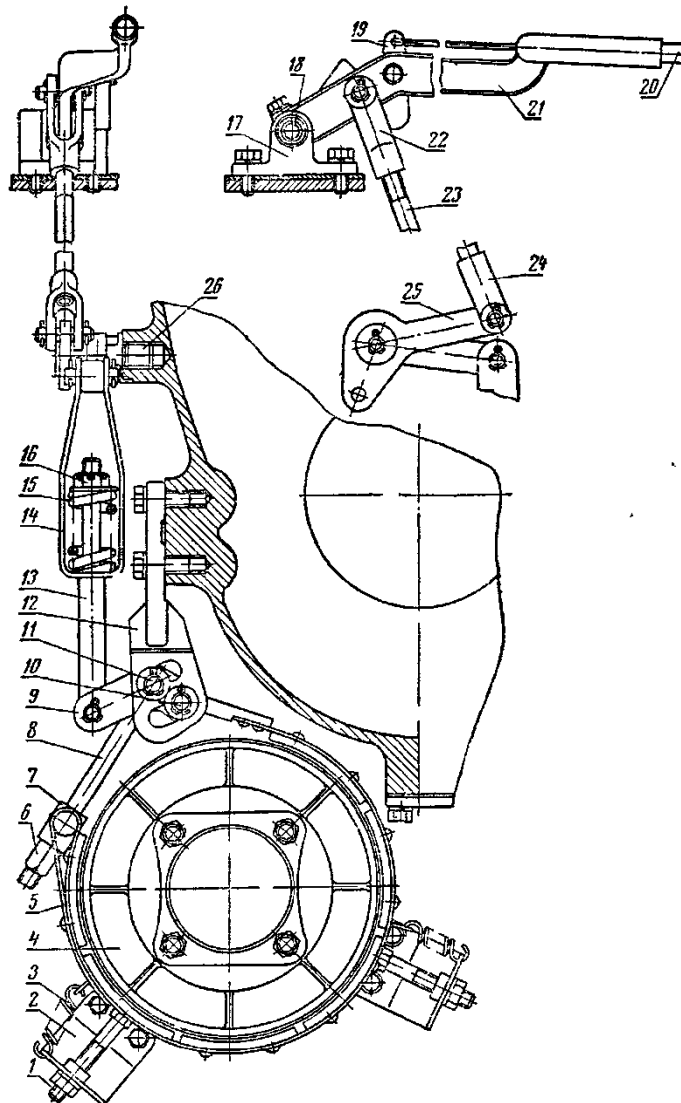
Центральный тормоз: 1 – регулировочный болт; 2, 12 и 17 – кронштейны; 3 – оттяжная пружина; 4 – барабан; 5 – лента и тормоза; 6 и 15 – гайки; 7 – втулка; 8 – регулировочная тяга; 9 и 25 – двуплечие рычаги; 10 и 11 – пальцы; 13 – тяга компенсатора; 14 – корпус компенсатора; 15 – пружина компенсатора; 18 – ось рычага управления; 19 – защелка; 20 – кнопка; 21 – рычаг управления; 22 и 24 – вилки; 23 – тяга.
